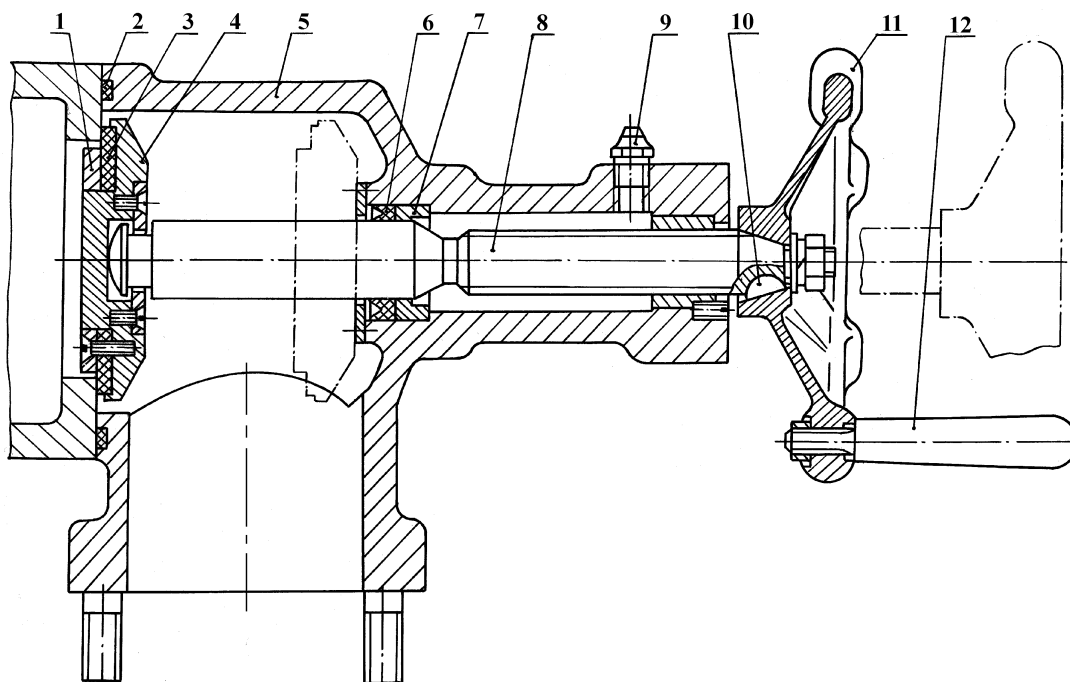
Вентиль напорный нормального давления: 1 – накладка; 2 – кольцо уплотнительное; 3 – уплотнительное кольцо; 4 – корпус клапана; 5 - корпус вентиля; 6 – манжета; 7 - втулка направляющая; 8 – винт; 9 – масленка; 10 - шпонка сегментная; 11 – маховик; 12 - рукоятка
